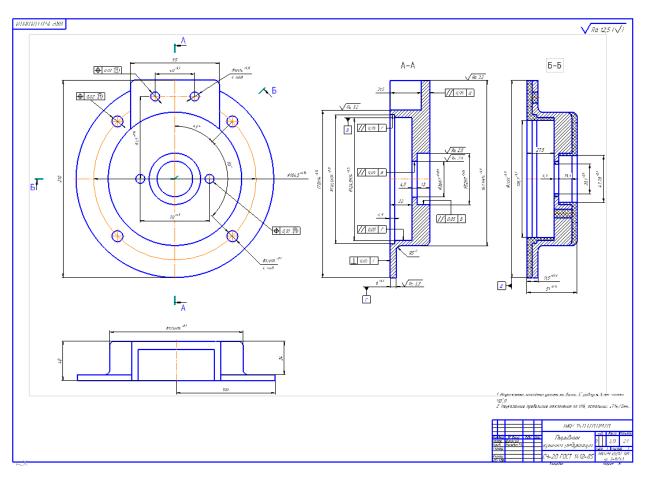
Чертеж детали «Передняя крышка редуктора»
